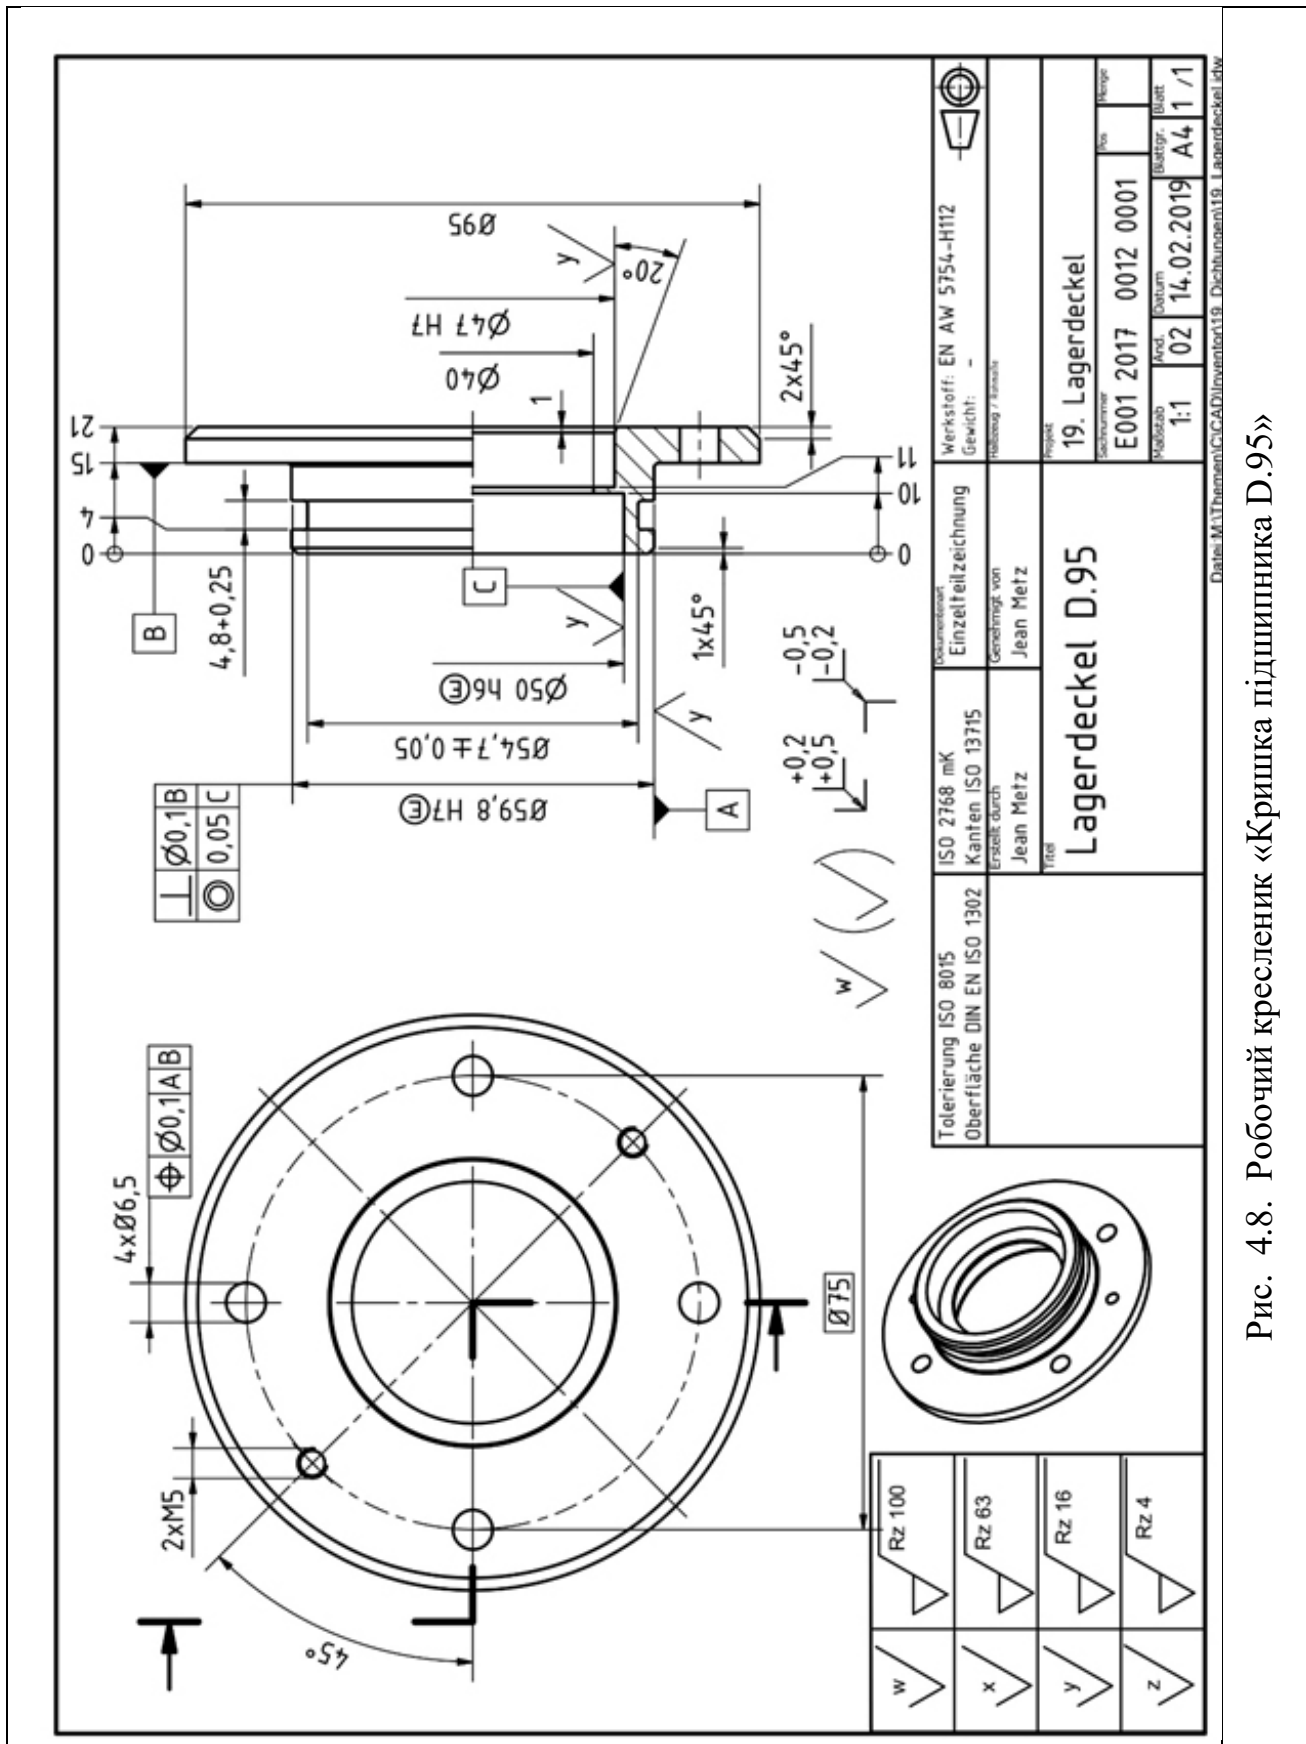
Робочий кресленик «Кришка підшипника D.95»
